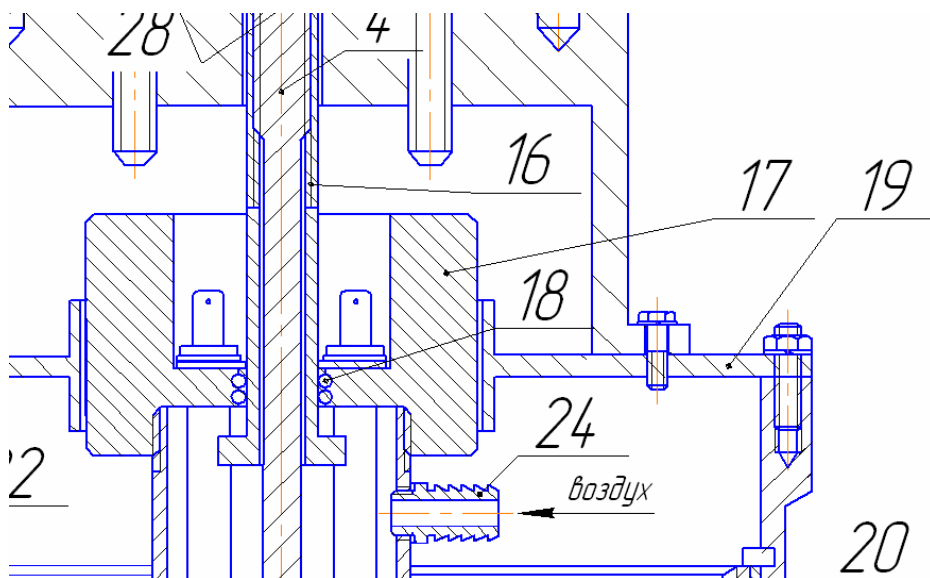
Расположение резиновых уплотнительных колец в крышке корпуса клапана
